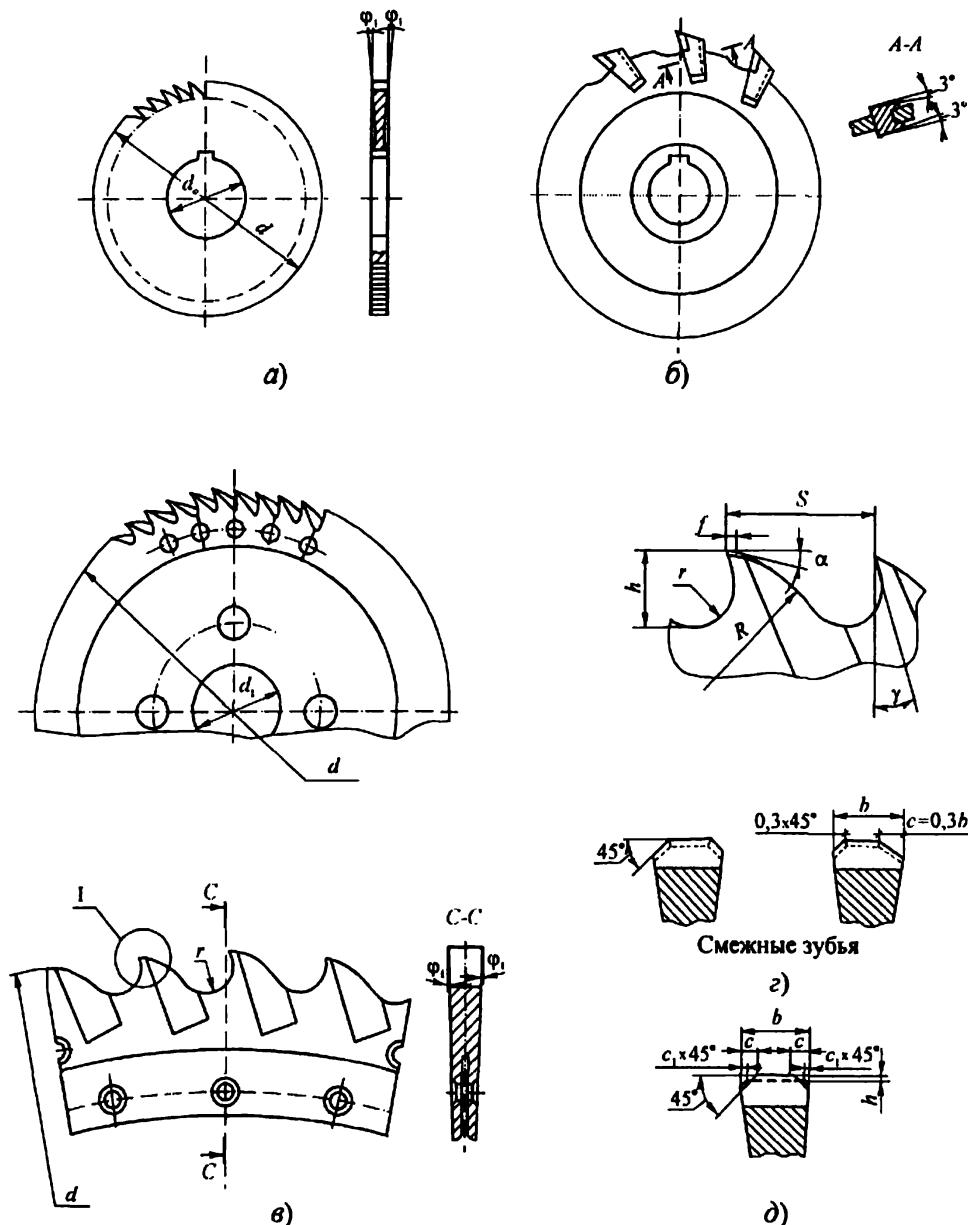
Фрезы прорезные и отрезные: а – цельная; б – отрезная сборная; в – сегментная; з, д – схемы резанья
